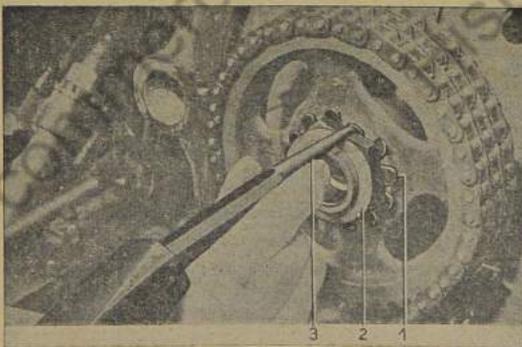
Sechskantmutter für Nockenwellenrad entsichern
